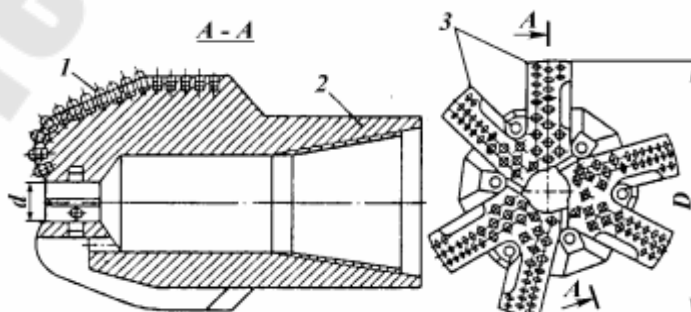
Шестилопастная бурильная головка типа ИСМ, оснащенная вооружением из сверхтвердого сплава «славутич»: 1 – вставки из сверхтвердого сплава «славутич» со сферической рабочей поверхностью; 2 – корпус с шестью лопастями, керноприемным каналом и шестью промывочными каналами.
